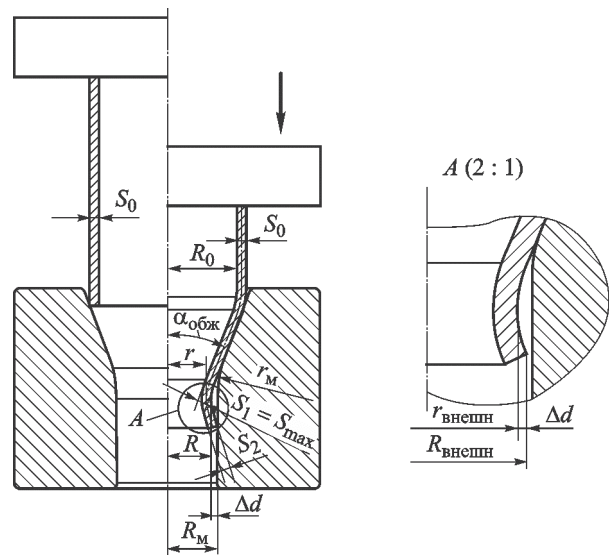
Схема обжима трубчатой заготовки в коническую матрицу с выходом в цилиндрическую часть
